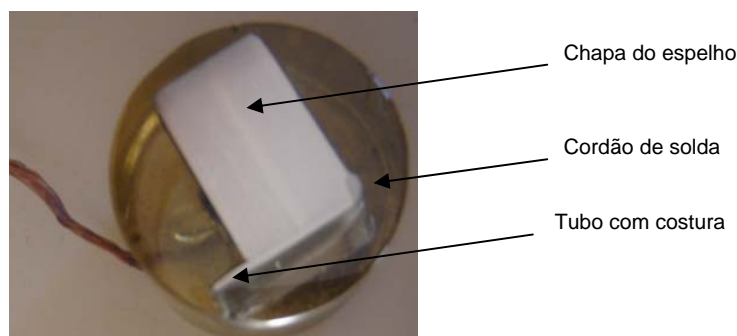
Preparação da junta tubo-espelho soldada para o ensaio de sensibilização.
